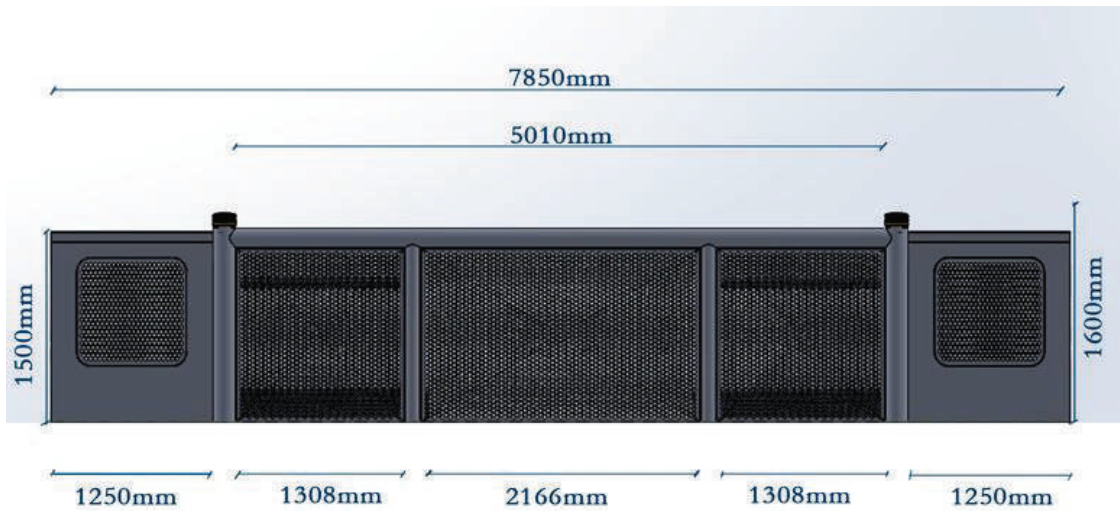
Dimensionamento frontal 2. Fonte: Pelo autor
